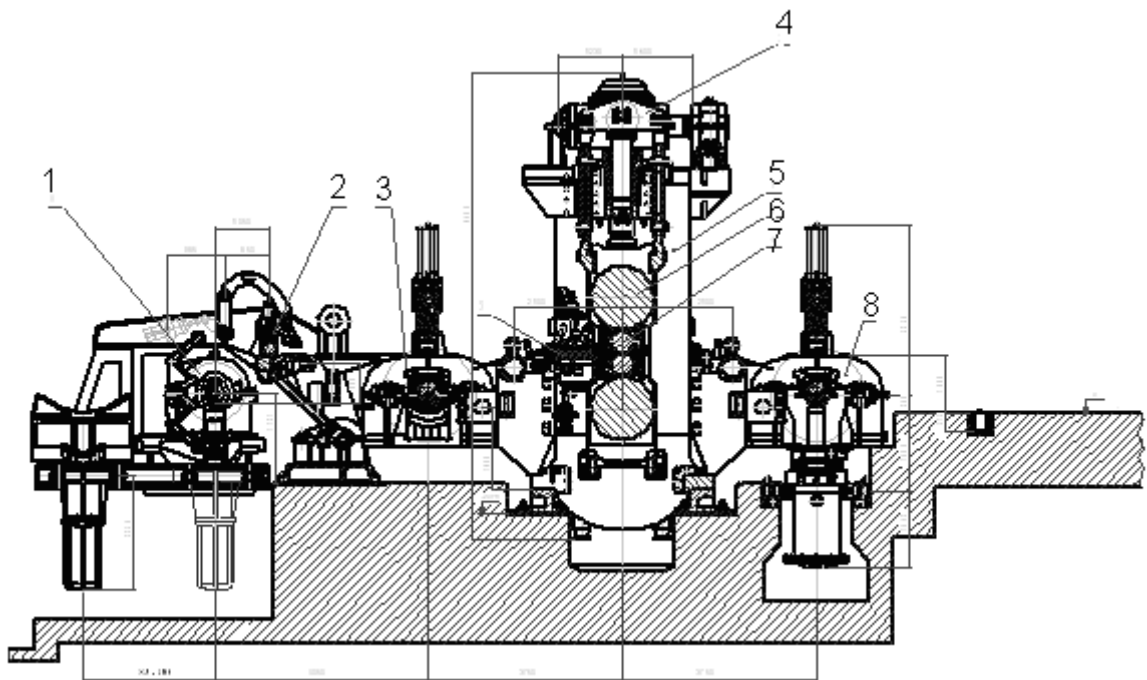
Реверсивний стан 1200: 1 – розмотувач; 2 – відгинач; 3 – ліва моталка; 4 – натискний механізм; 5 – прокатна кліть; 6, 7 – робочі та опорні валки; 8 – права моталка
